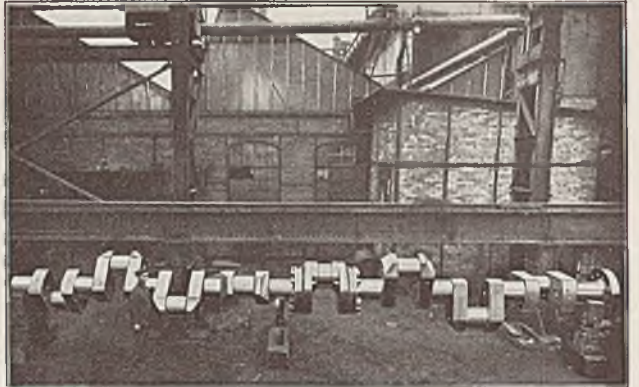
Eine 8fach gekröpft Kurbelwelle mit Kompressorwelle in der Mitte, für und fertig bearbeitet und geflanscht, 19000 kg Gewicht, 10500 mm Länge, für MAN geliefert
